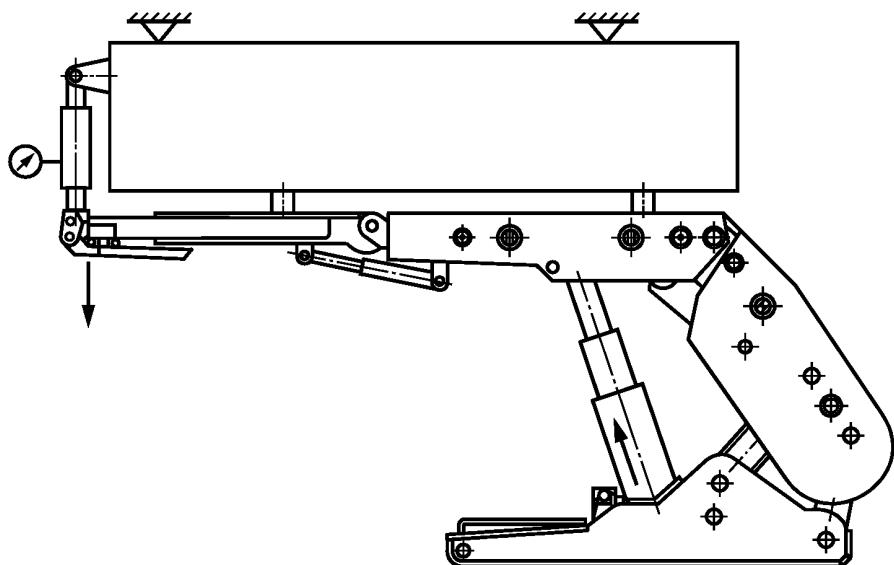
Схема нагружения для определения сопротивления на конце гидроподжимной консоли перекрытия пенального типа
